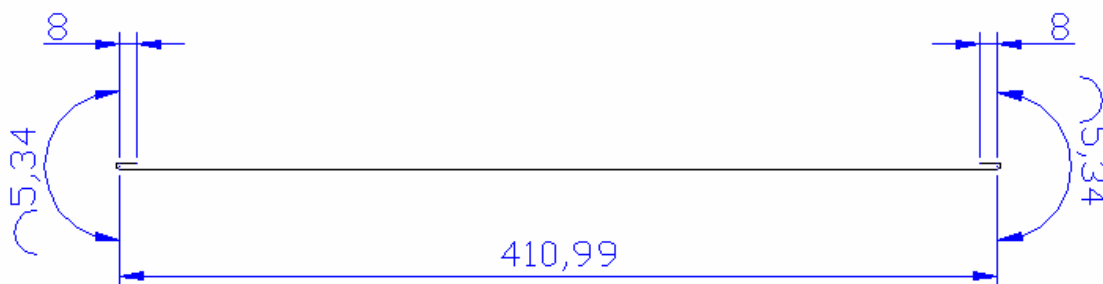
Longitud de la secció longitudinal de la xapa exterior
